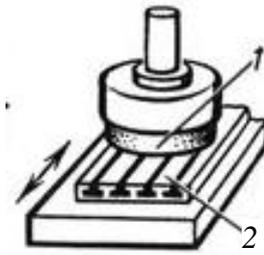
Шлифование плоской поверхности торцевой поверхностью круга: 1 – шлифовальный круг; 2 – заготовка
